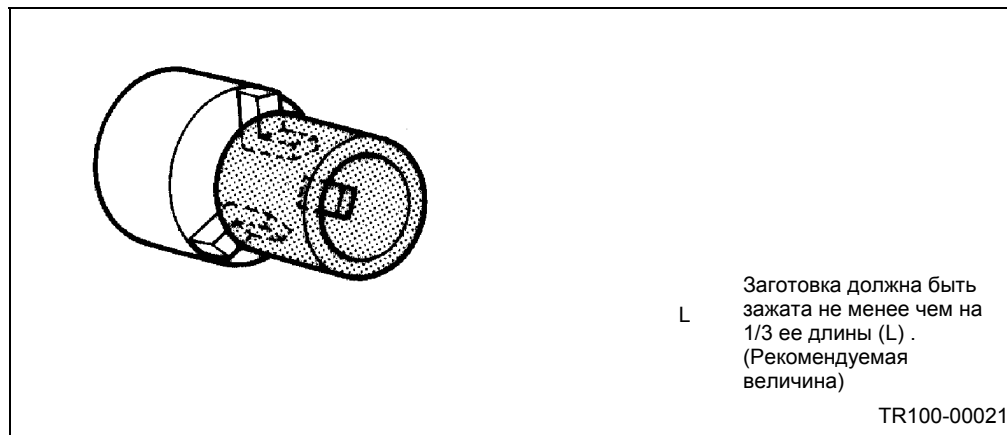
Обработка мягких кулачков (захват заготовки по внутреннему диаметру)
